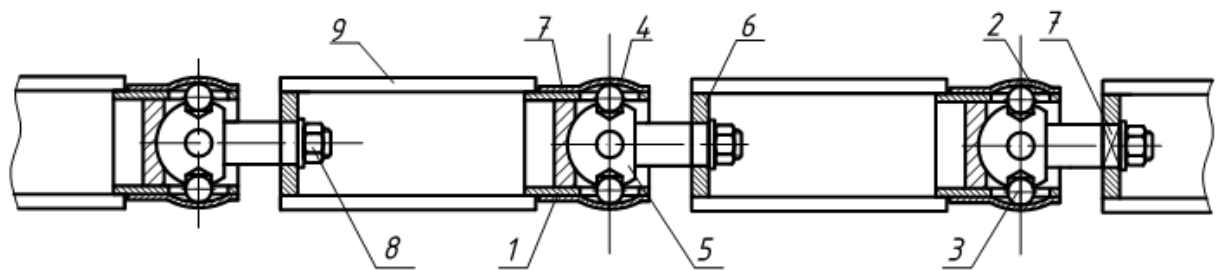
Конструктивна схема гвинтового секційного шарнірного робочого органу
